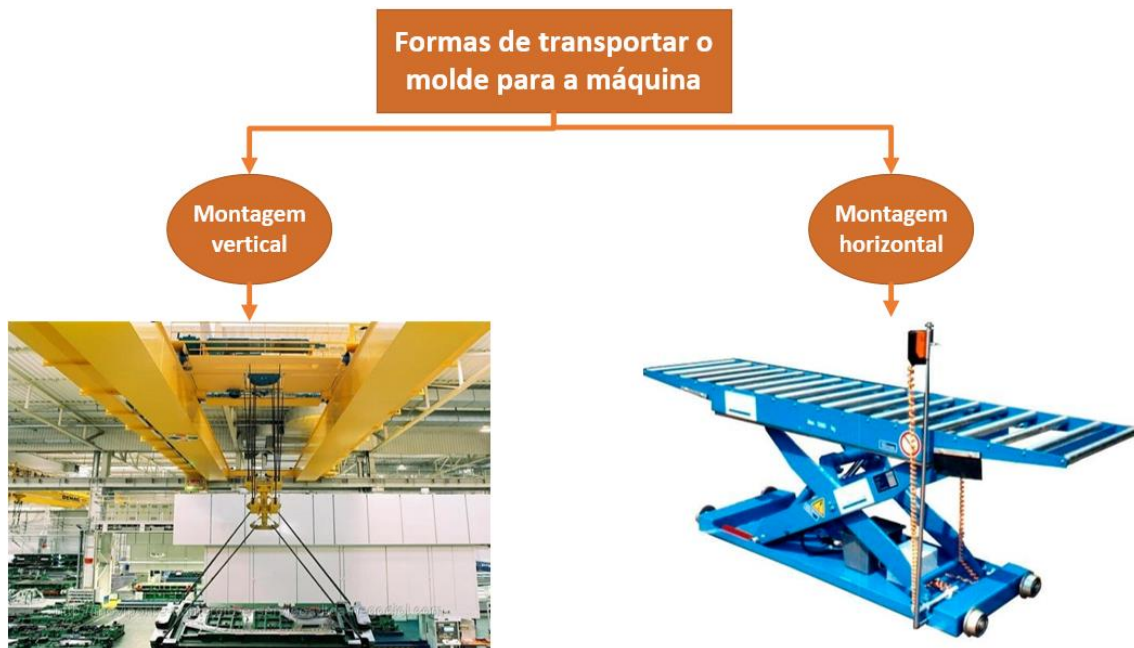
Formas de montagem dos moldes nas máquinas de injeção [14,15]
